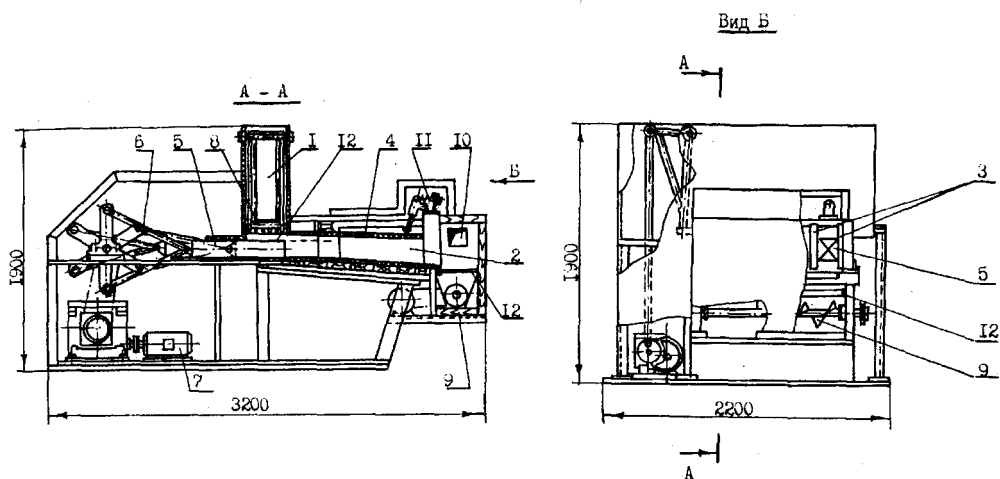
Конструктивно-технологическая схема установки с горизонтальными рабочими камерами и кривошипно-шатунным механизмом привода поршней уплотнения.
